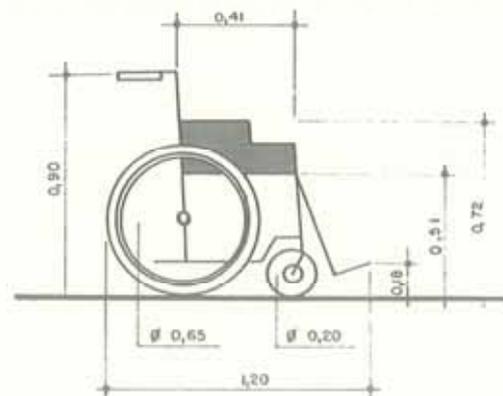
CADEIRA DE RODAS — VISTA LATERAL
